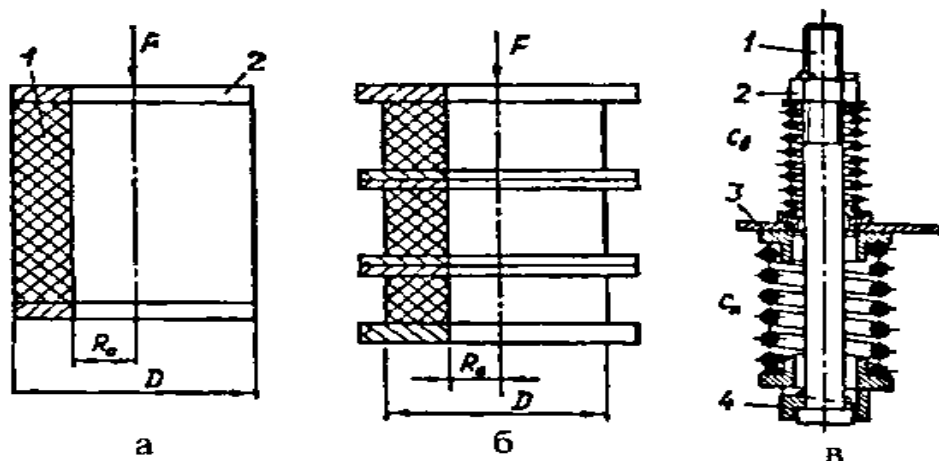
Пружні опори вібромашин: а, б — гумометалеві; в — металеві
